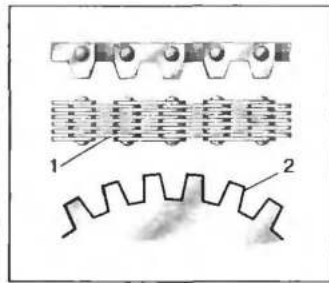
Зубчатая цепь привода распределительного вала: 1 — цепь; 2 — звездочка
